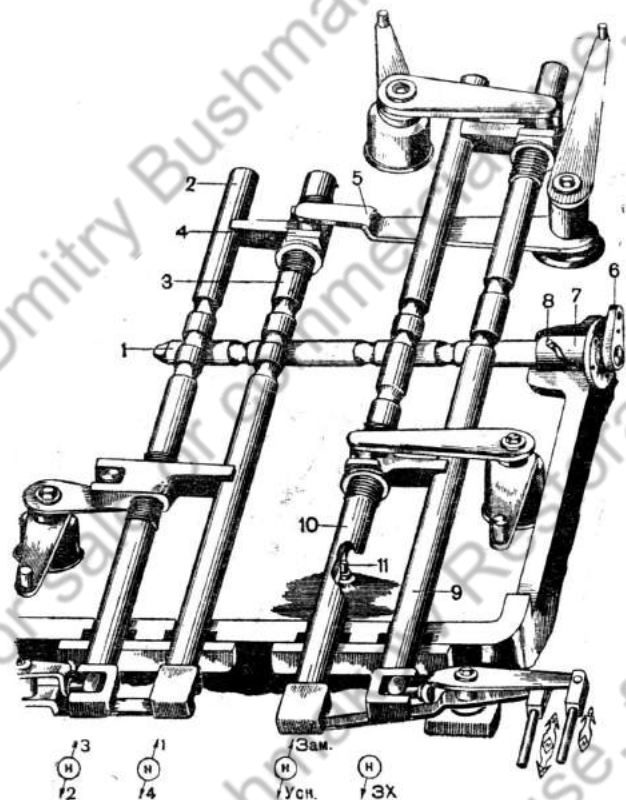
Замковый механизм коробки перемены передач: 1 — стержень замка; 2 — поводковый валик 2-й и 3-й передач; 3 — поводковый валик 1-й и 4-й передач; 4 — вилка поводкового валика; 5 — двухплечий рычаг; 6 — рычаг замка; 7 — втулка; 8 — штифт; 9 — поводковый валик заднего хода; 10 — поводковый валик демультипликатора; 11 — стопор поводкового валика
